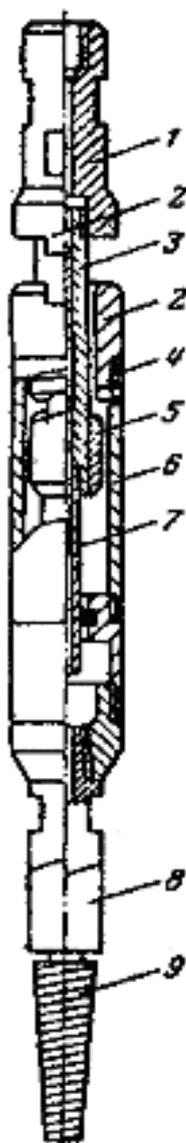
Механический вибратор: 1 – переходник; 2 – кулачок; 3 – шток; 4, 5 – верхняя и нижняя зубчатые полумуфты; 6 – корпус; 7 – трубка; 8 – отсоединитель труболовки; 9 – межчик
